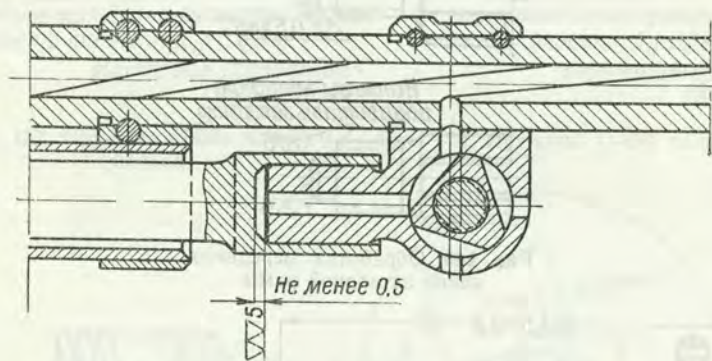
Зачистка заднего среза патрубка газовой камеры
